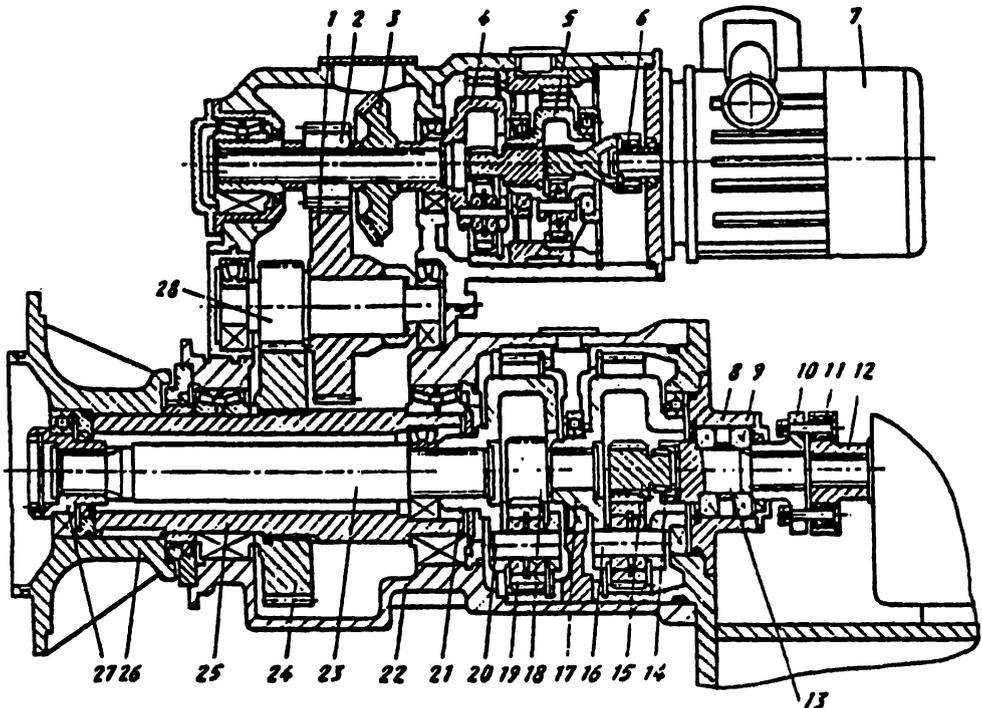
Редуктор исполнительного органа комбайна «Урал-20А»
